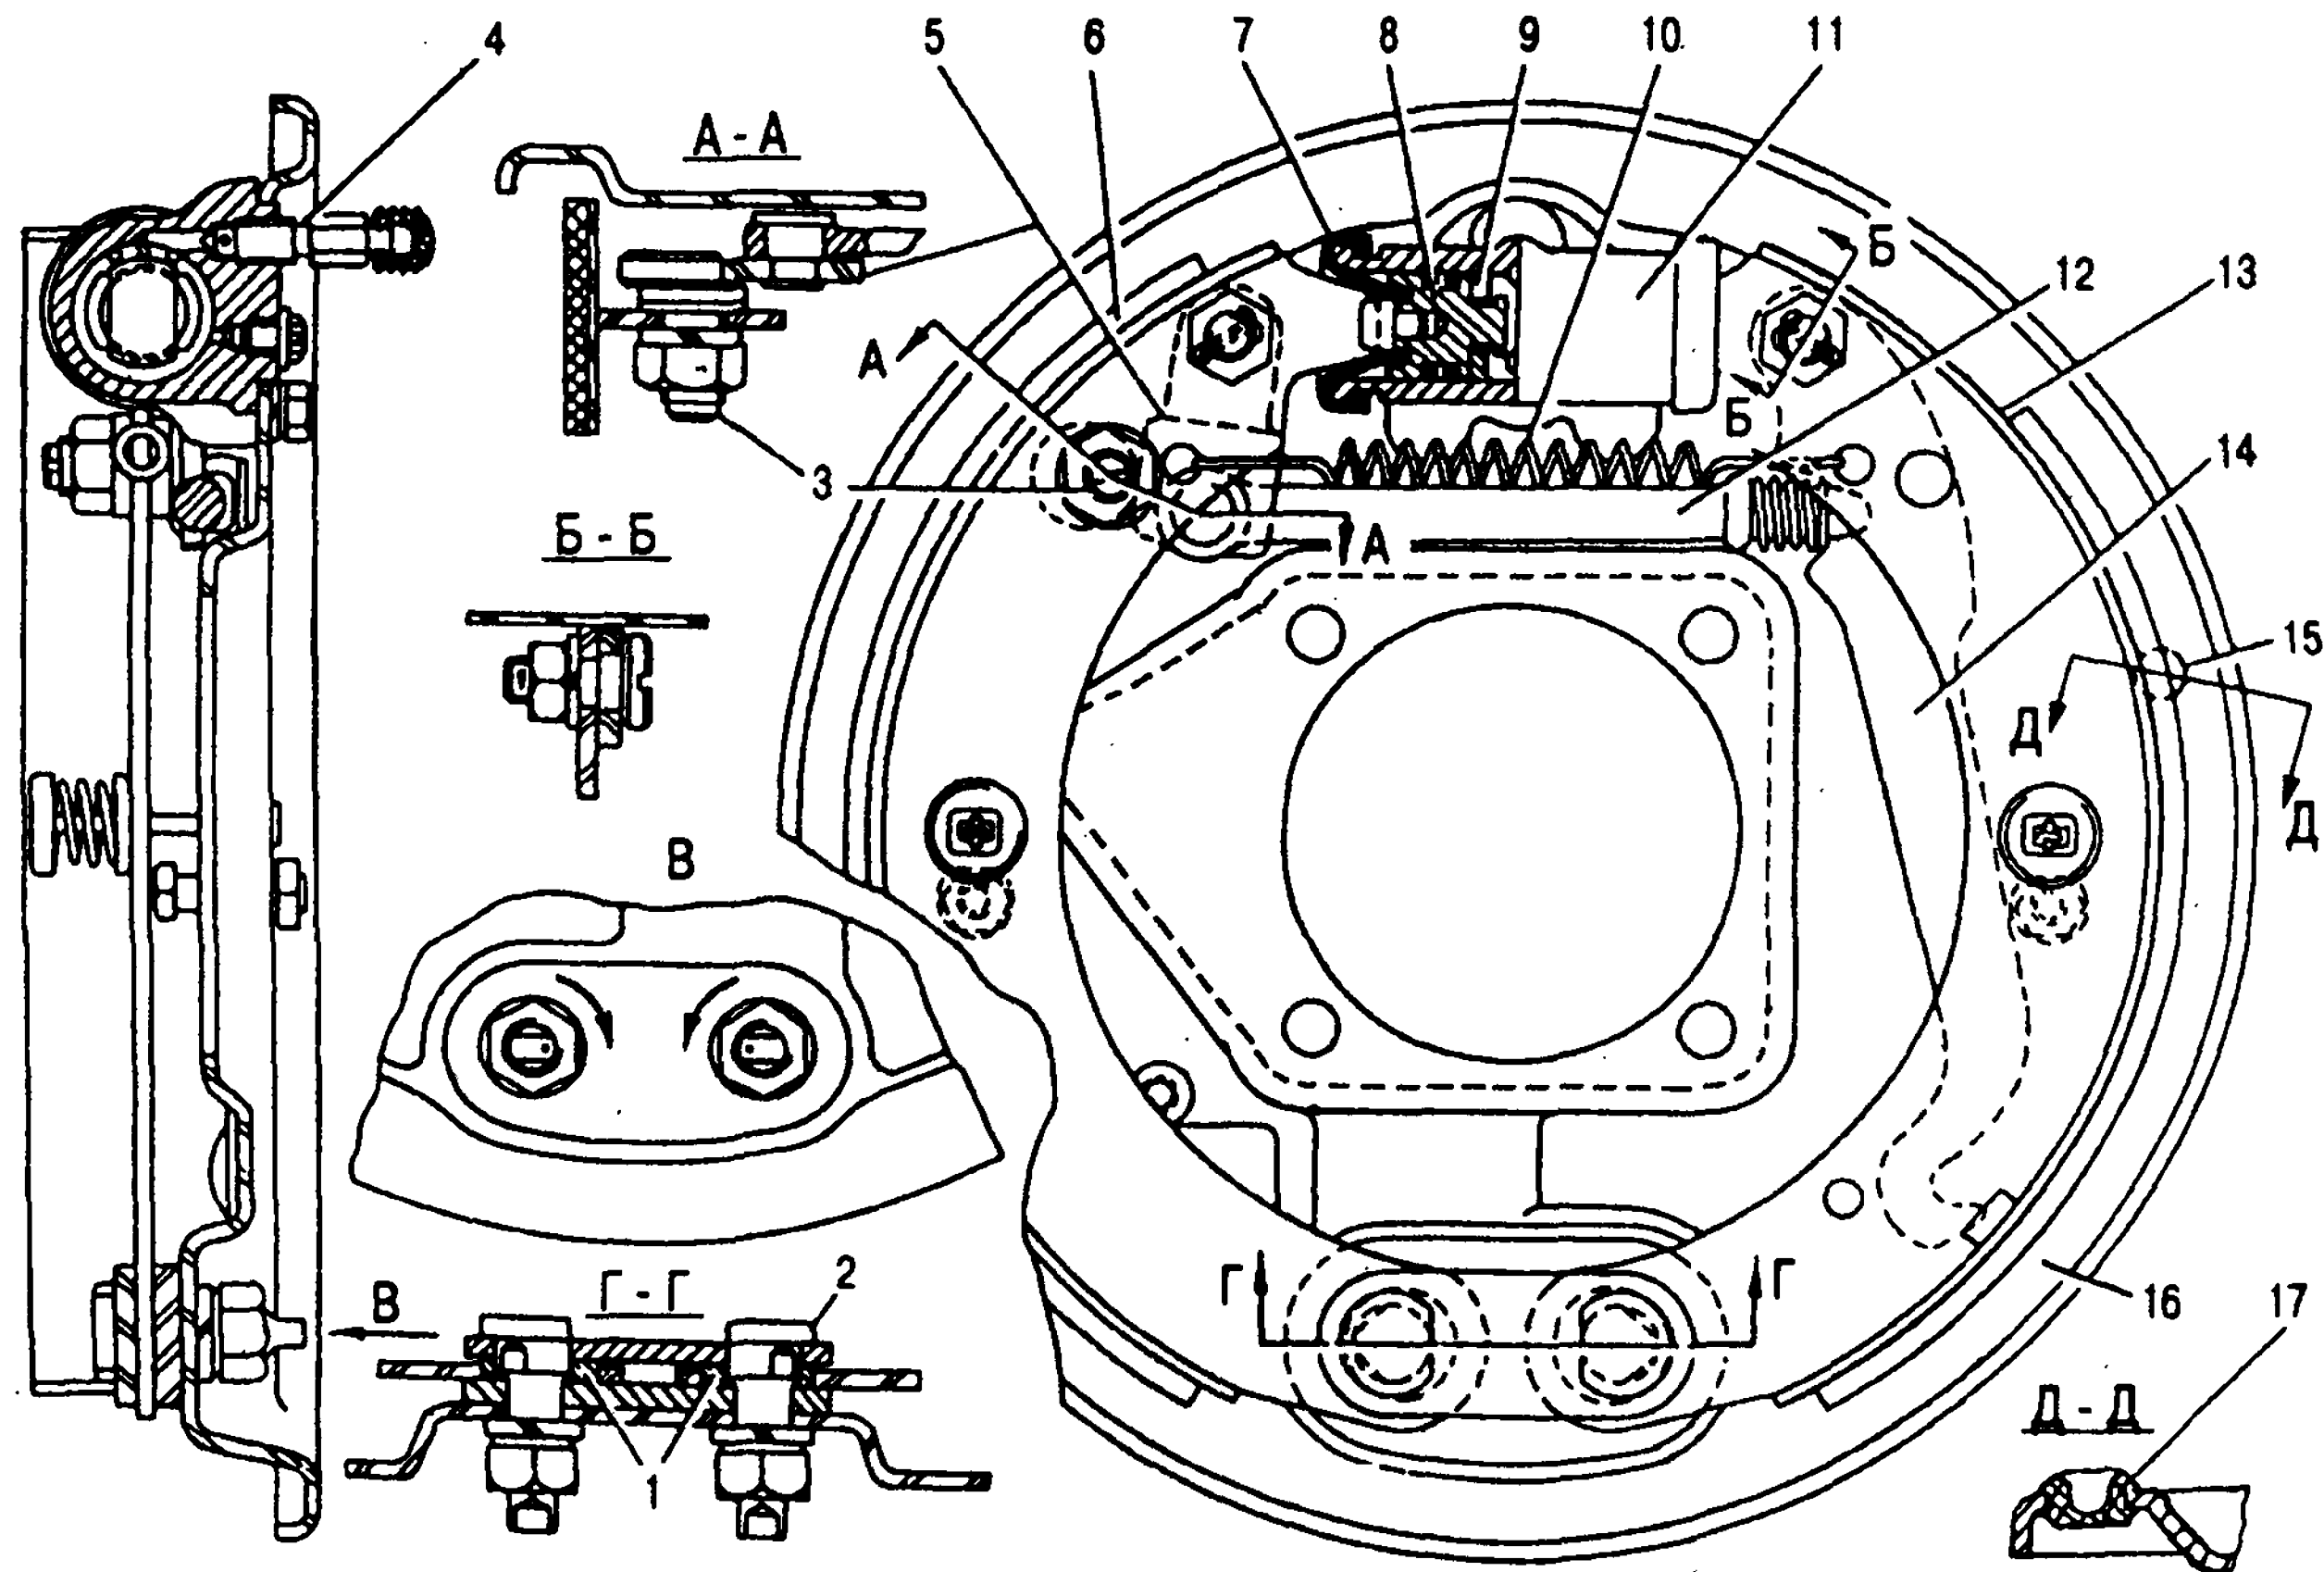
Тормозной механизм задних колес: 1 - эксцентрик опорных пальцев; 2 - опорный палец; 3 - регулировочный эксцентрик стояночного тормоза; 4 - клапан прокачки с защитным колпачком; 5 - маятниковый рычаг; 6 - передняя колодка; 7 - защитный чехол; 8 - поршень; 9 - упорное кольцо; 10 - стяжная пружина; 11 - колесный цилиндр; 12 - разжимной стержень; 13 - задняя колодка; 14 - приводной рычаг стояночного тормоза; 15 - отверстие для контроля износа тормозных накладок; 16 - щит; 17 - заглушка
